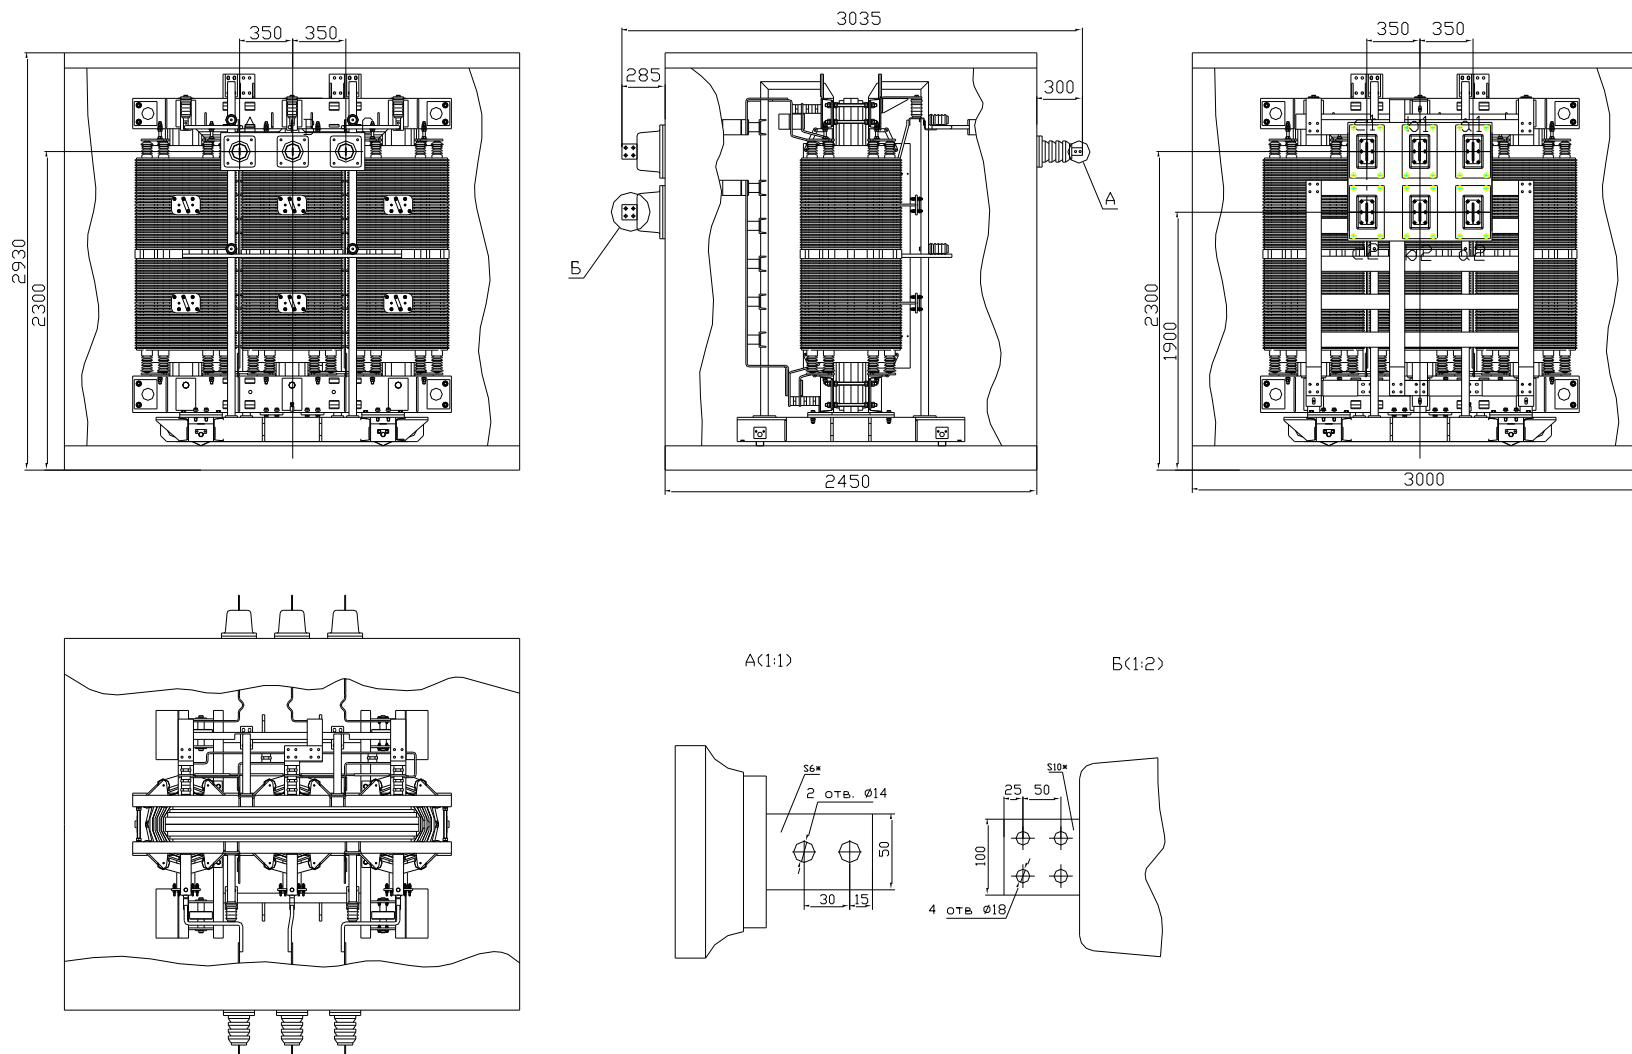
Габаритный чертеж трансформатора ВДУ
